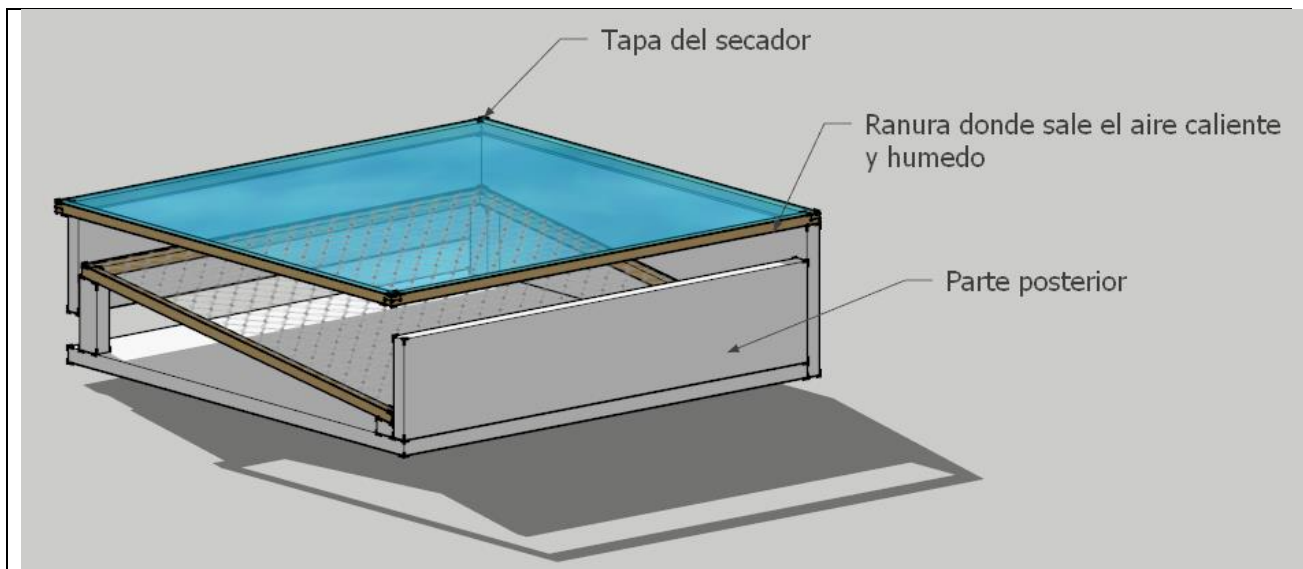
Vista posterior del secadero donde se detallan las ranuras de entrada y salida de aire.
